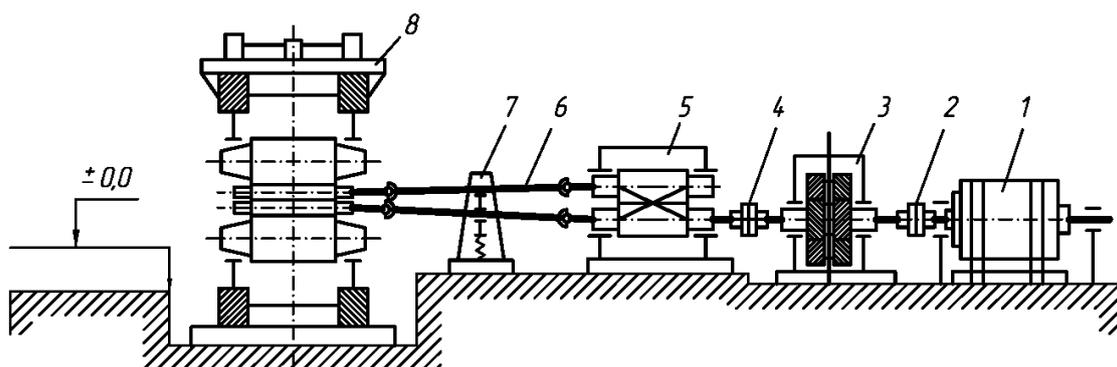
Главная линия прокатного стана: 1—электродвигатель; 2—моторная муфта; 3—редуктор; 4—коренная муфта; 5—шестеренная клетка; 6—шпиндели; 7—уравновешивание шпинделей; 8—рабочая клетка.
